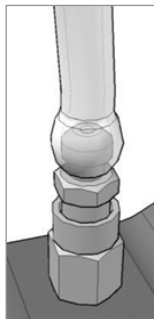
Entlüftungsschraube mit aufgestecktem Klarsichtschlauch
